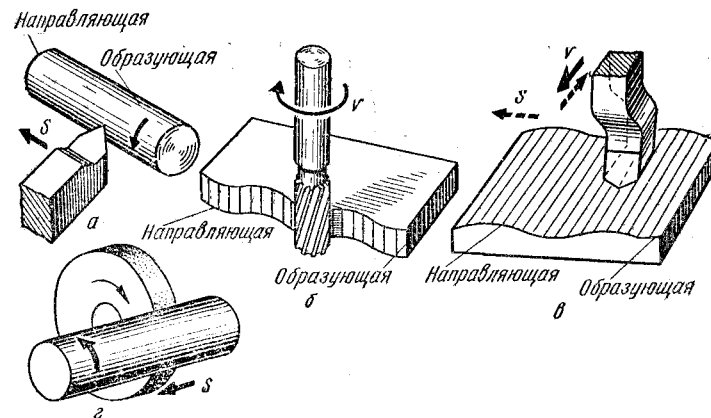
Методы обработки поверхностей деталей резанием: а — точение; б — фрезерование; в — строгание; г — шлифование
